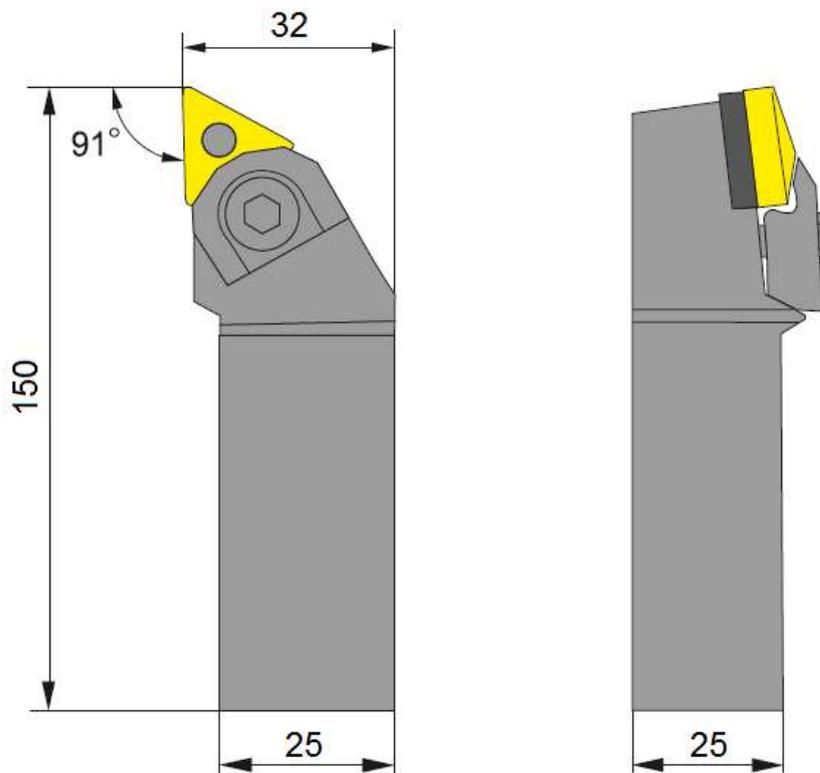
Резец PTGNR 2525 M16-03
